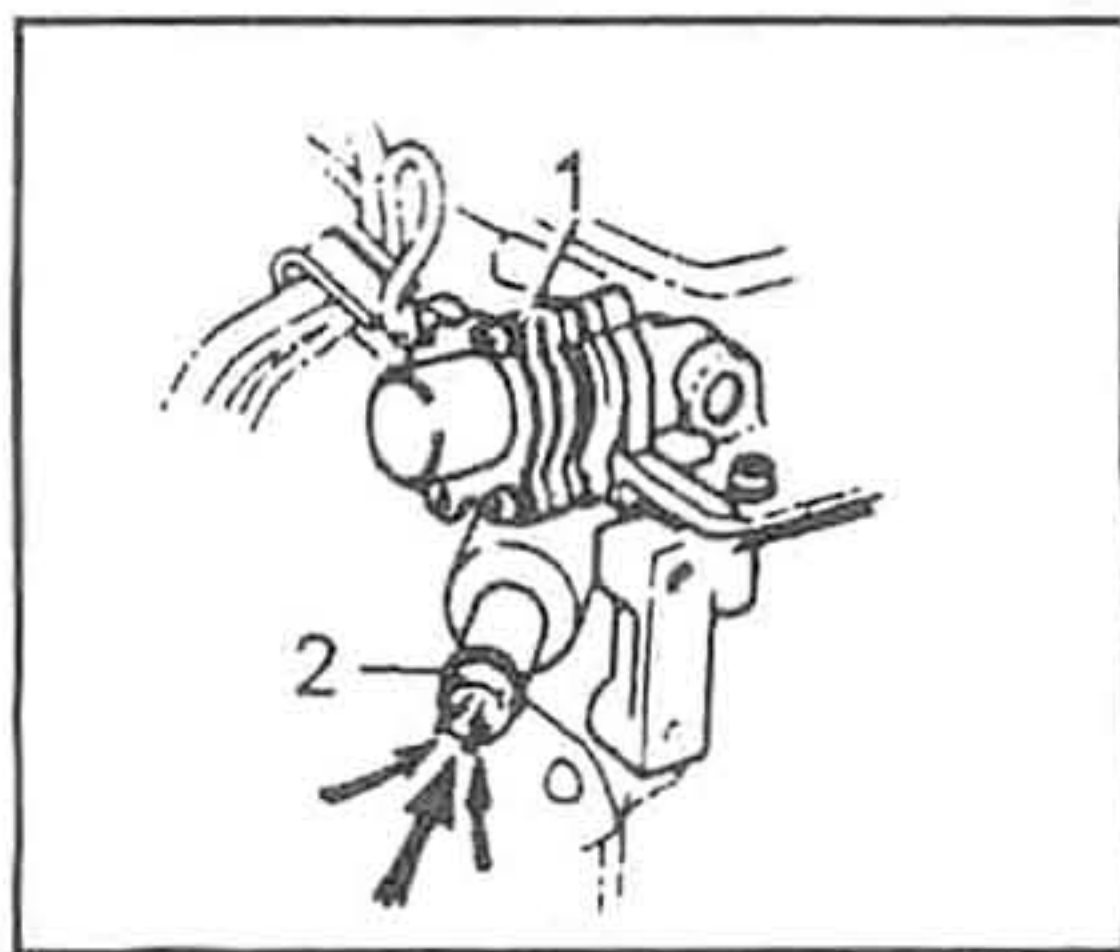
1. Клапан управления наружной вентиляцией. 2. Трубка наружной вентиляции (открыта).
